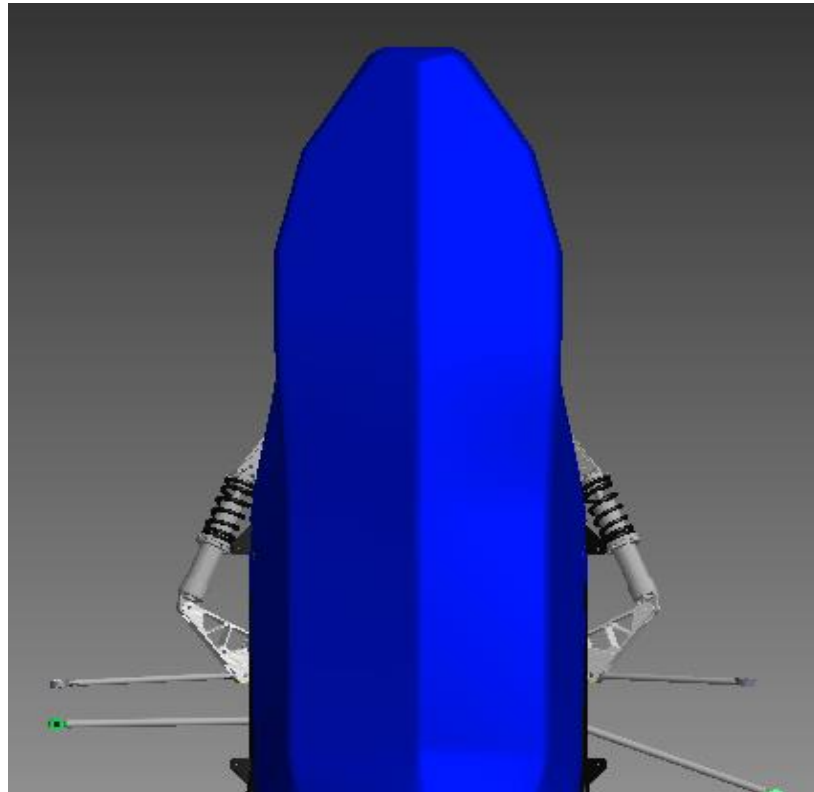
Grundrisszeichnung Entwurf 4 - Vorderachse
